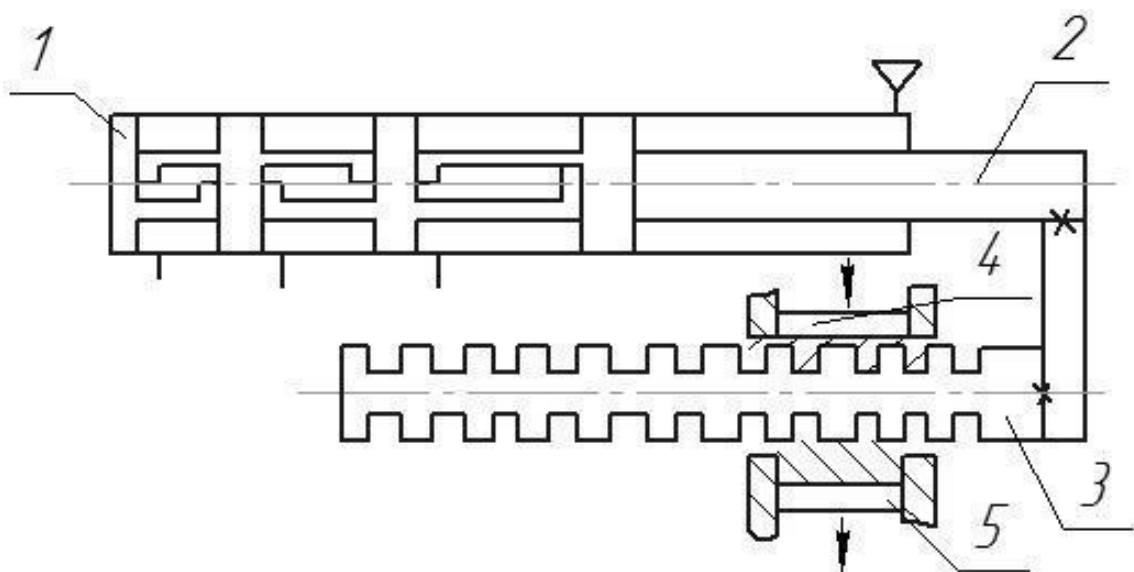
Механічний напрямний пристрій типу кардної стрічки
